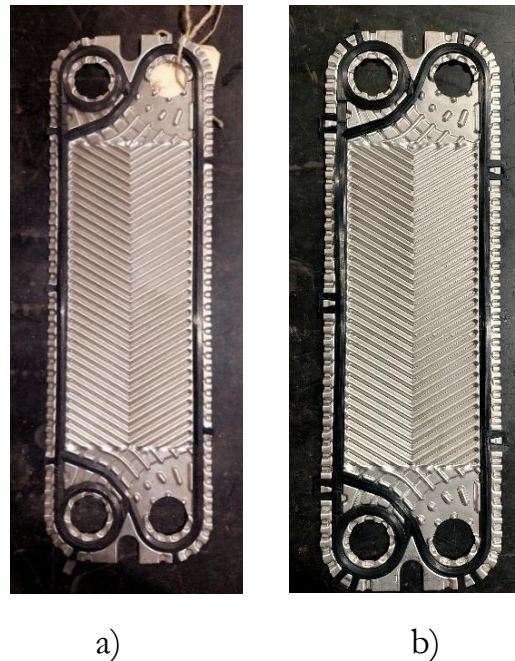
Placas Skills: a) Placa com "Groove-in"; b) Placa com "Hook lock".
